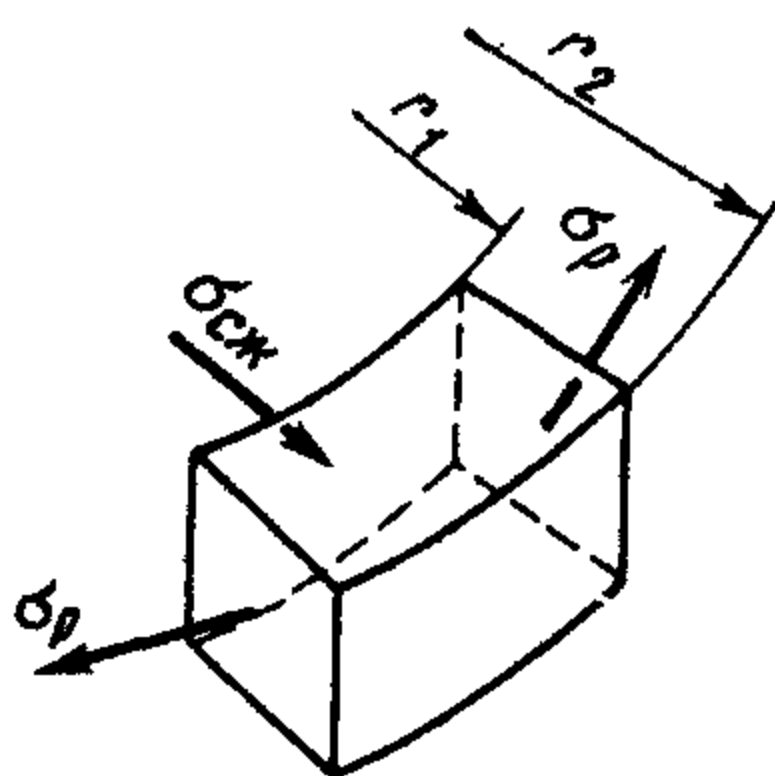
Напряжения, действующие на элемент стенки цилиндрической втулки
